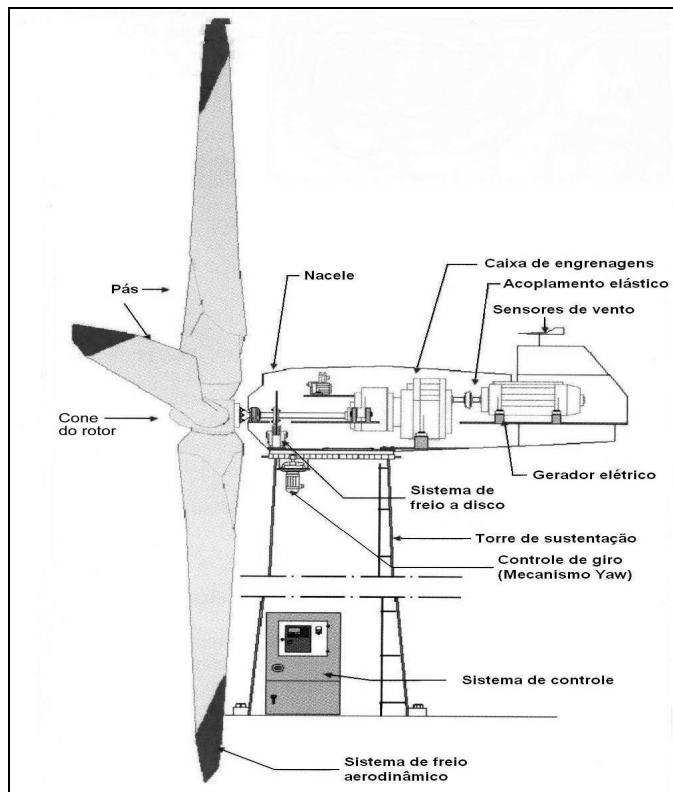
Principais componentes de um aerogerador de eixo horizontal
